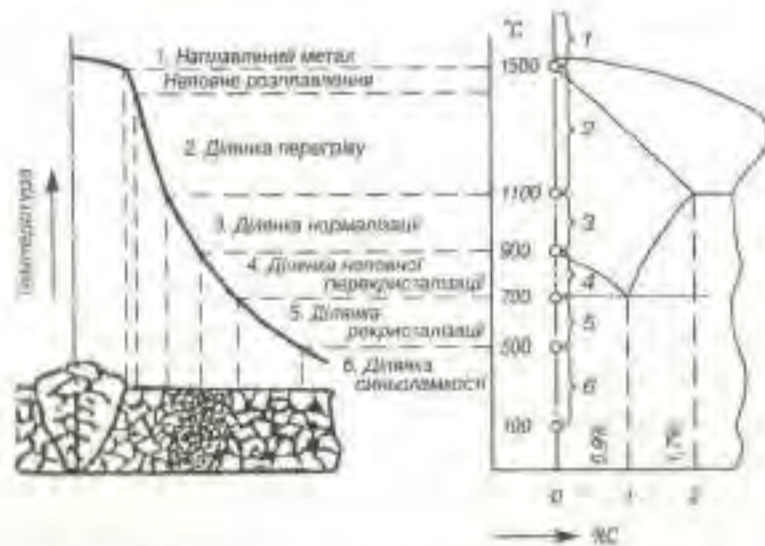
Будова зони термічного впливу зварного з'єднання
